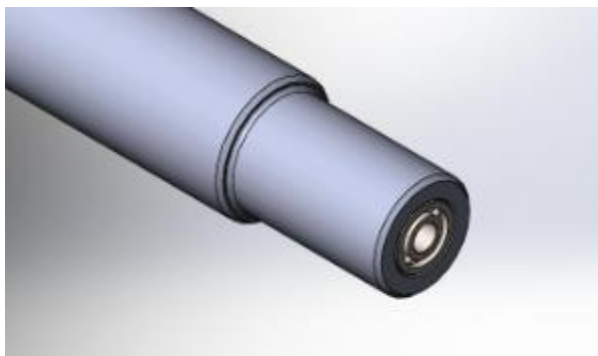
Підшипники на торцях валу барабана стрічкового дозатора модернізованої конструкції
